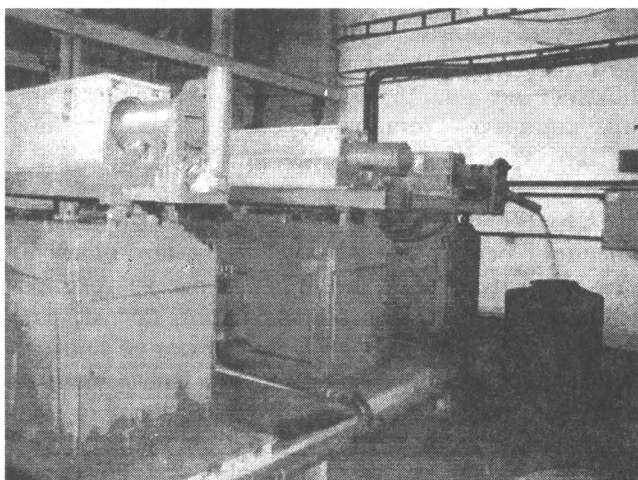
Общий вид участка сталелитейного цеха №2 РУП "МАЗ" термической обработки стальной литой дроби при индукционном нагреве
